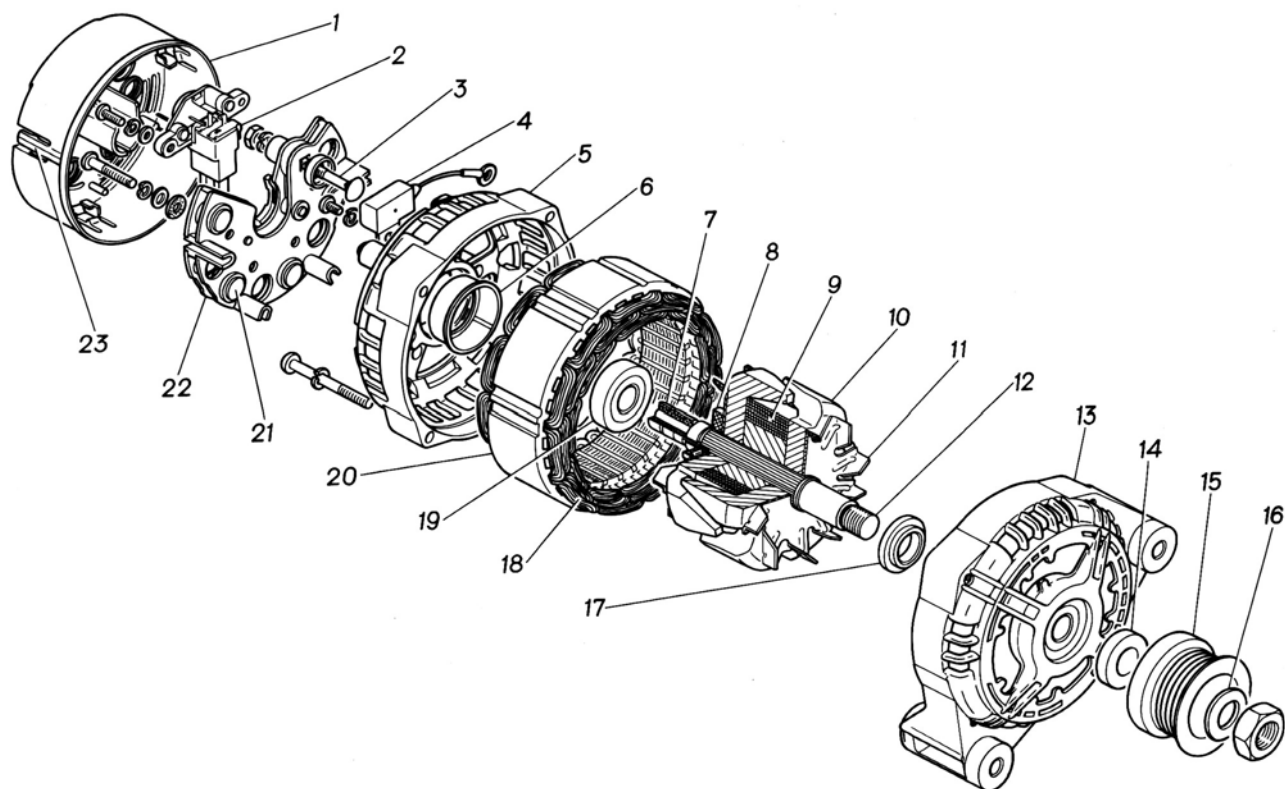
Генератор 9422.3701: 1 - защитный кожух; 2 - регулятор напряжения со щеткодержателем и щетками; 3 - контактный болт; 4 - конденсатор; 5 - крышка со стороны контактных колец; 6 - держатель подшипника; 7 - контактные кольца; 8 - изолятор; 9 - обмотка возбуждения; 10 - ротор; 11 - вентилятор; 12 - вал ротора; 13 - крышка со стороны шкива; 14 и 17 - втулки; 15 - шкив; 16 - тарельчатая шайба; 18 - обмотка статора; 19 - подшипник; 20 - статор; 21 - силовой диод; 22 - выпрямительный блок; 23 - держатель кожуха
